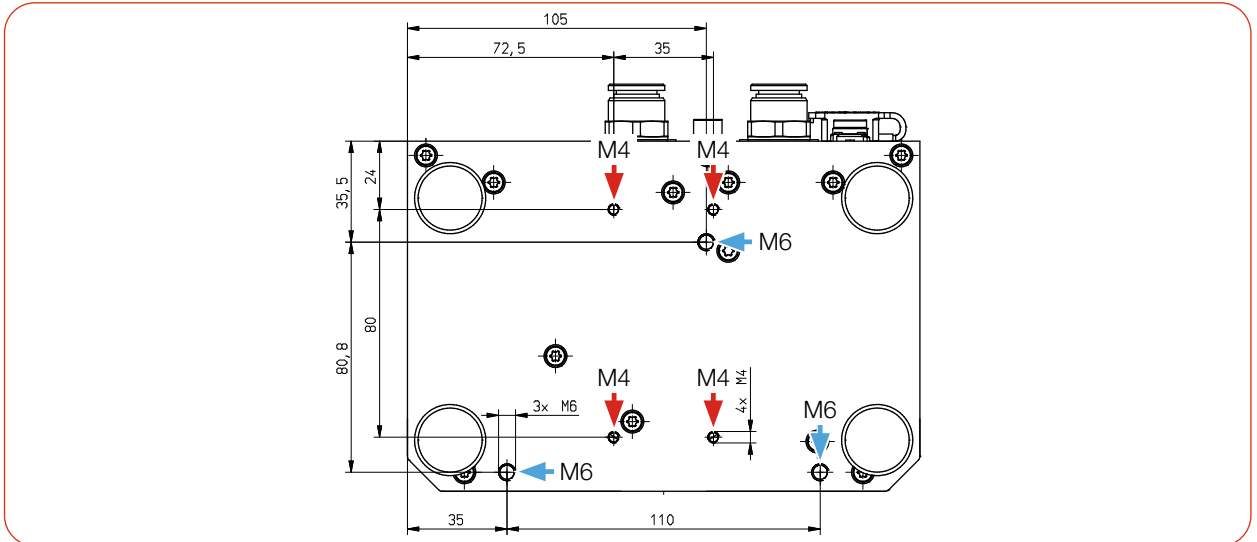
Befestigungsgewinde M4 und M6 im Boden des Gehäuses am CPM+ F-1 (Maße in mm)
